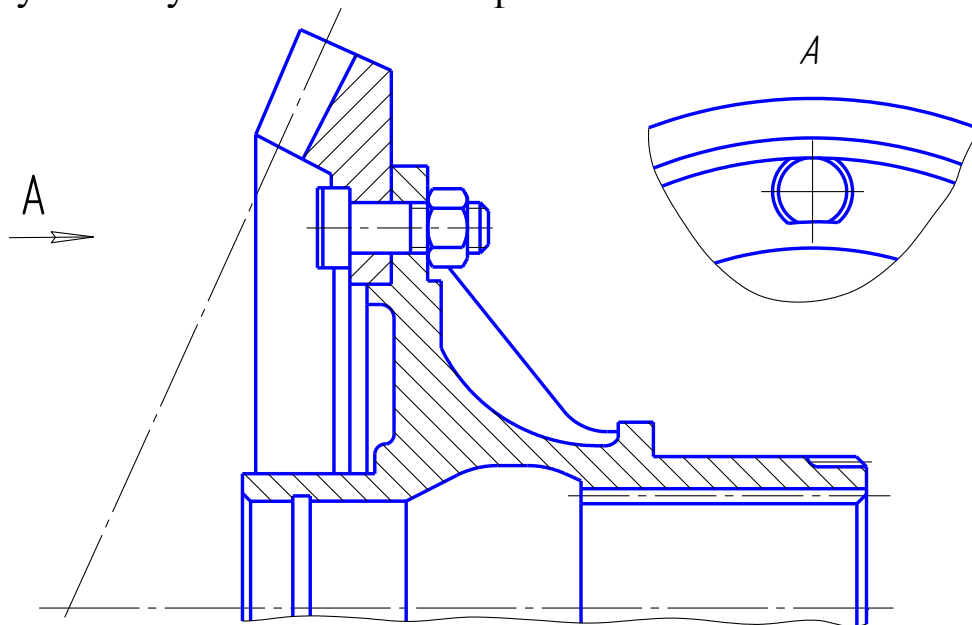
Соединение конического колеса с валом хвостового редуктора МИ – 4
